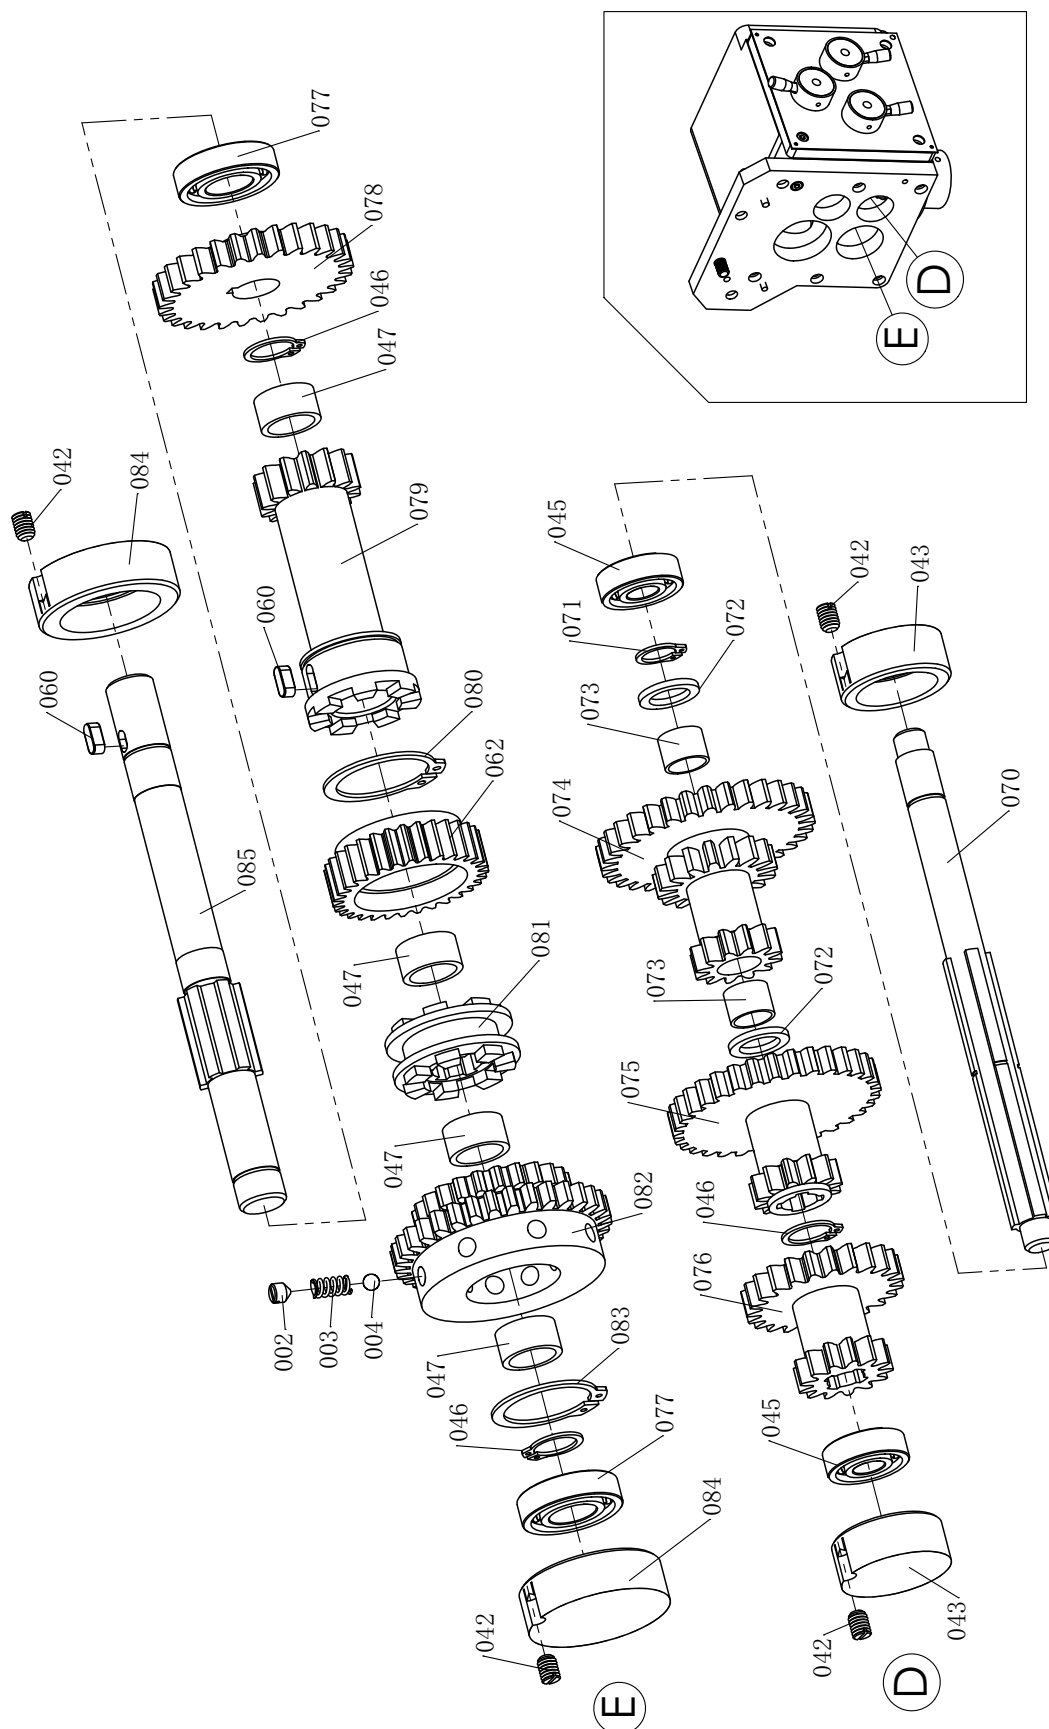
Vorschubgetriebe X-Achse - Feed gear X-Axis 3 - 3
